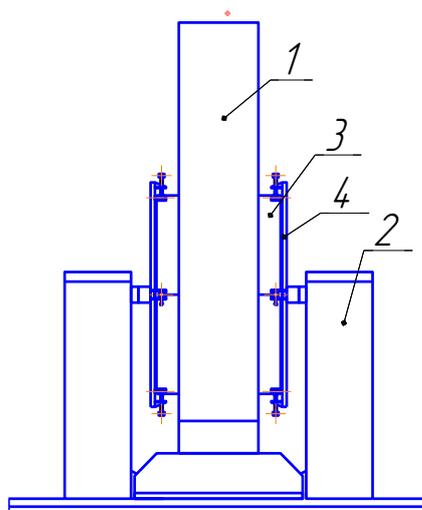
Сварка элементов обечайки:
